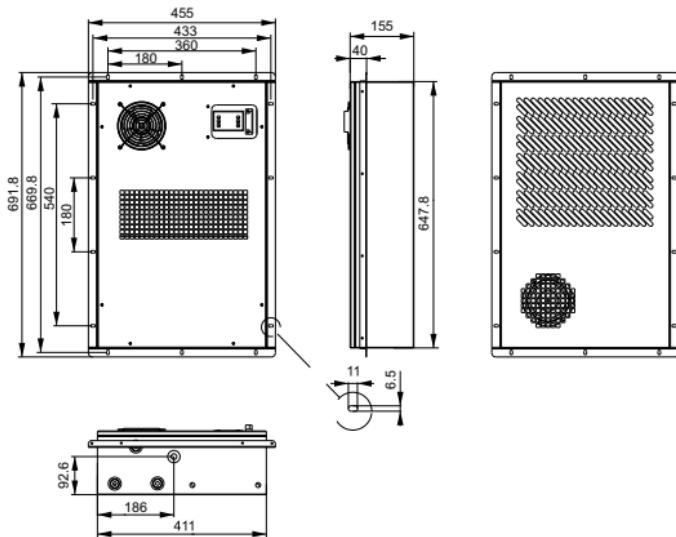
Внешний вид и габаритные размеры моделей СМ-0600-230 и СМ-0800-230 /
